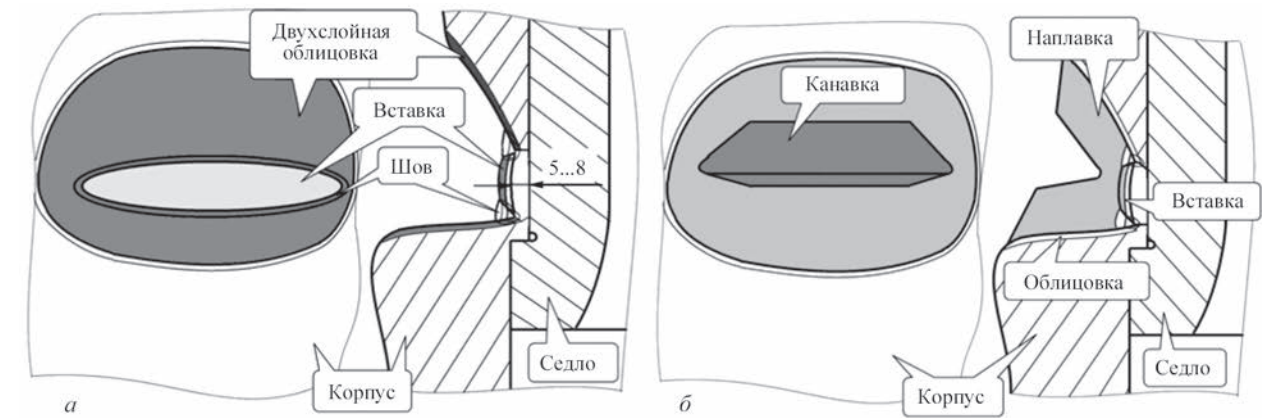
Разделка под сварку трещины в корпусе регулирующего клапана ЦСД и этапы ее заварки
